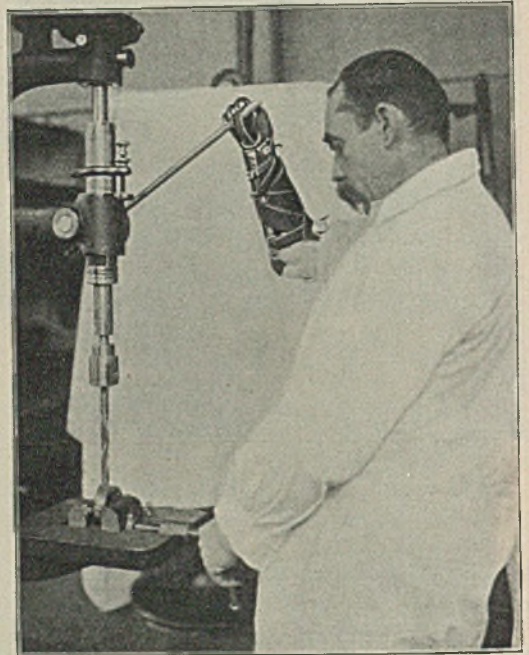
Bohren mit der Bohrmaschine (glatter zylindrischer Griff) von 20 mm Durchmesser.
